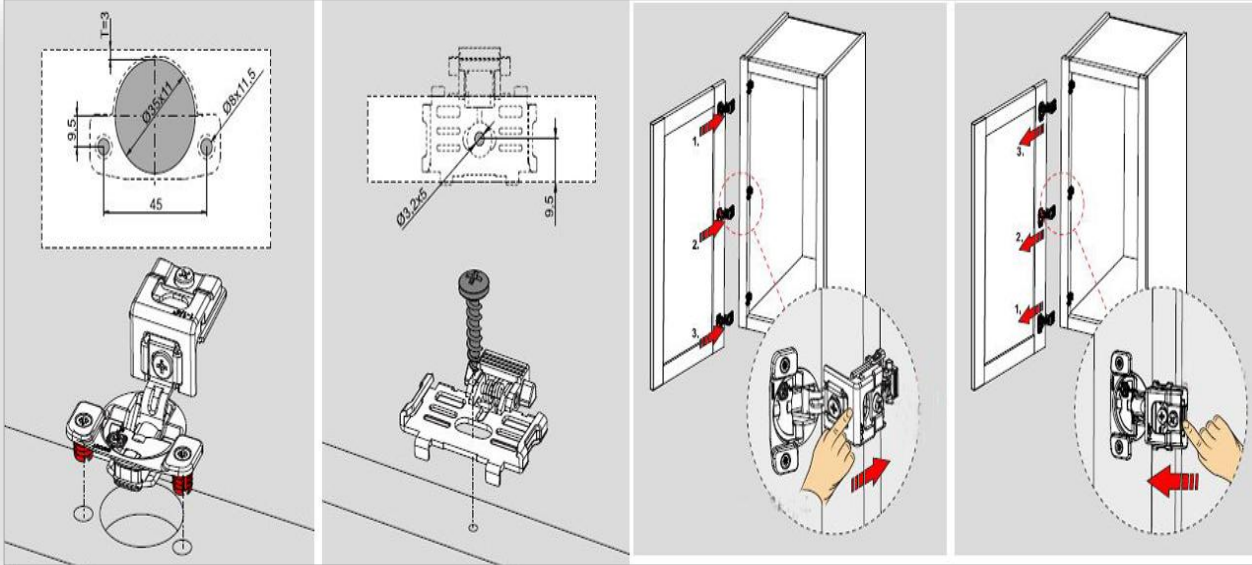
Avrupa ve Amerika tipi menteşelerde kullanılan bini örnekleri (URL-9)
